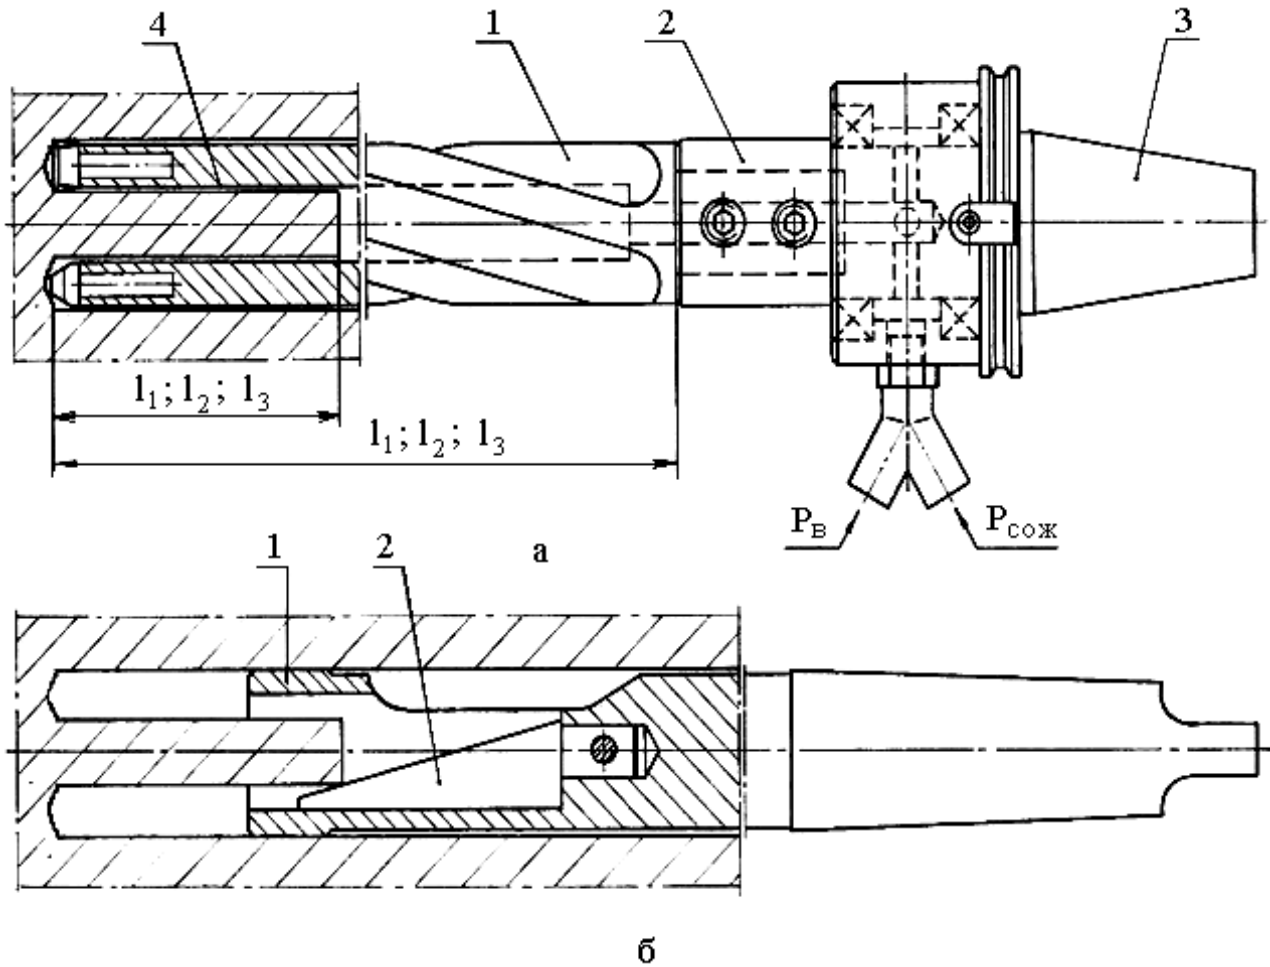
Инструмент для отбора проб с глубины до 500 мм:
